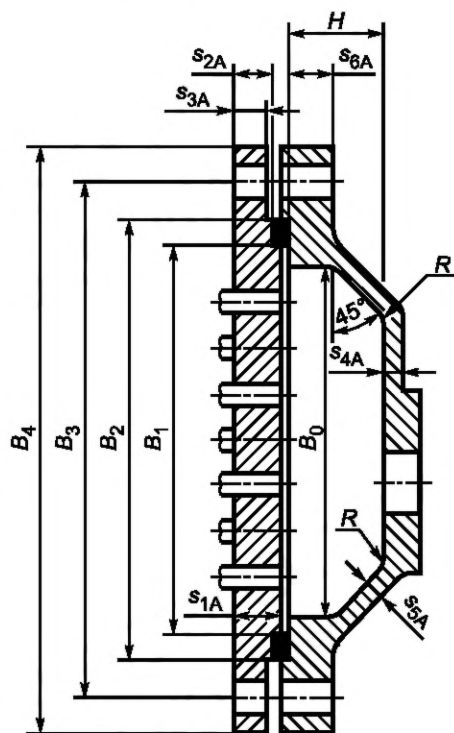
Камера разъемной конструкции с литой или штампованной крышкой
